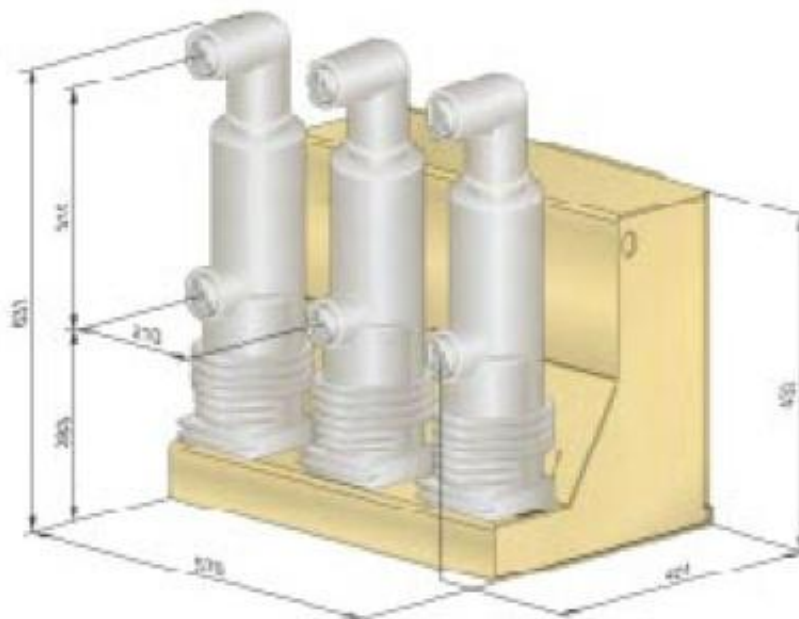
Внешний вид и габаритные размеры выключателя VM1
